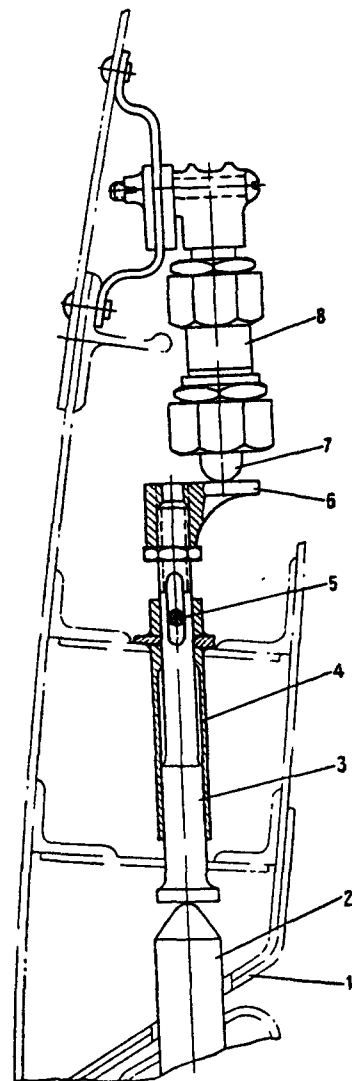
Бортовой аварийный люк (вид изнутри):
